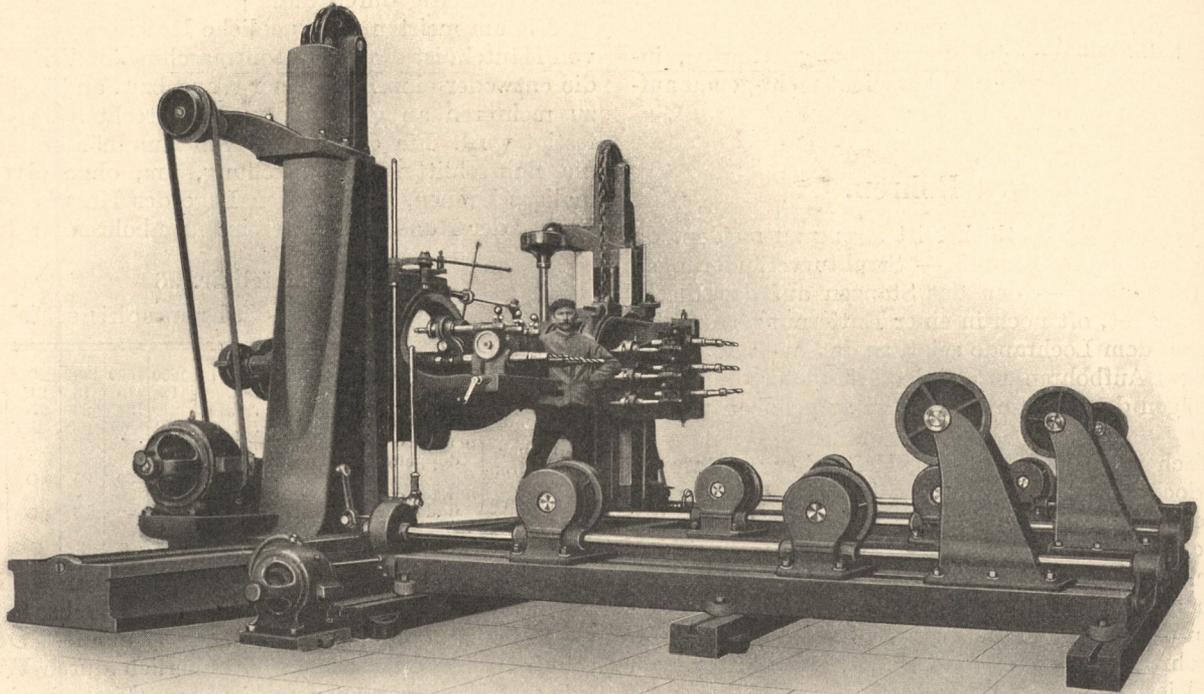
Doppelte Kesselbohrmaschine mit 6 Spindeln und Rollgang.
